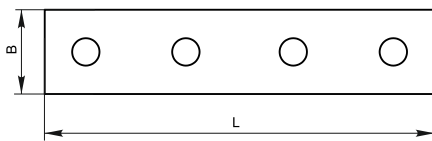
Пластина соединительная с 4 отверстиями для STRUT-профиля
